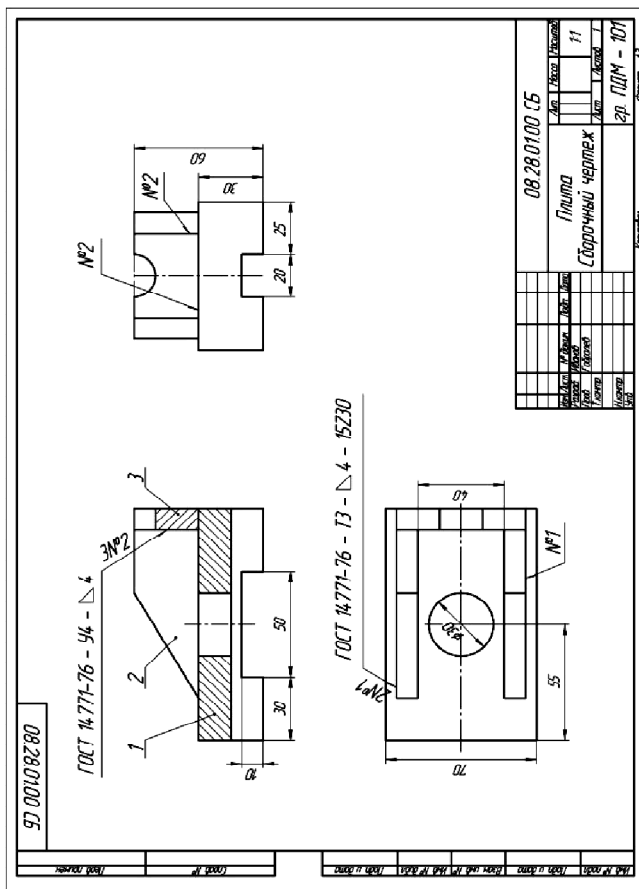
Пример выполнения сборочного чертежа сварного изделия
